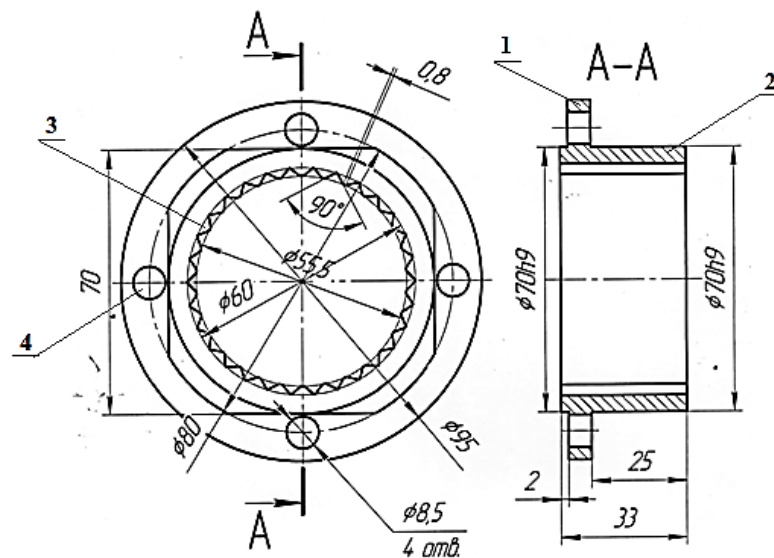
Конструкция храпового кольца поворотного механизма
